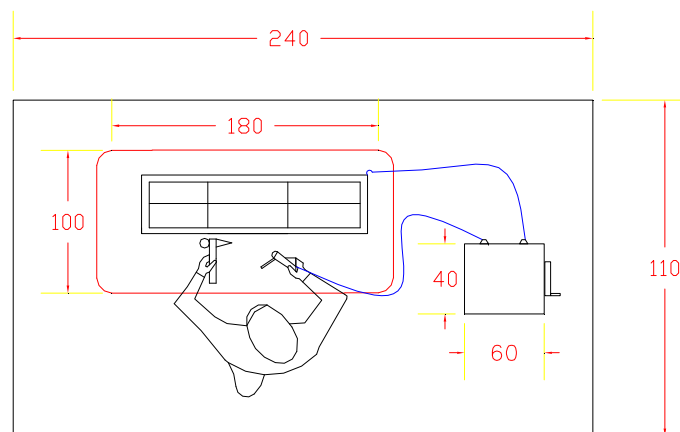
PUESTO DE TRABAJO DE SOLDADURA
